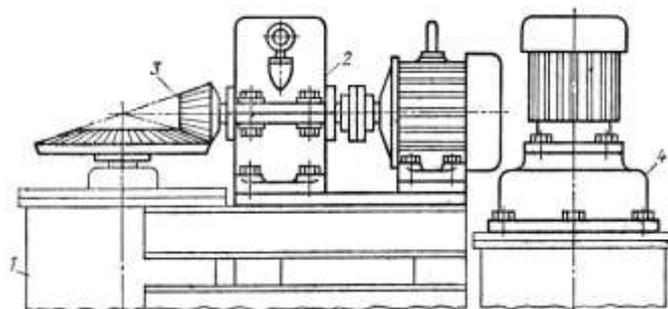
Уменьшение габаритных размеров и массы двухступенчатого редуктора
